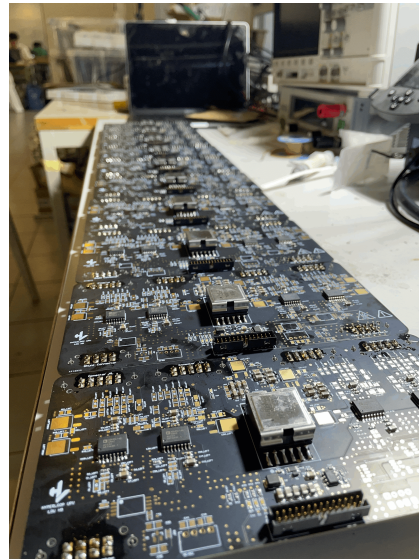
Proceso de soldadura LDU.
